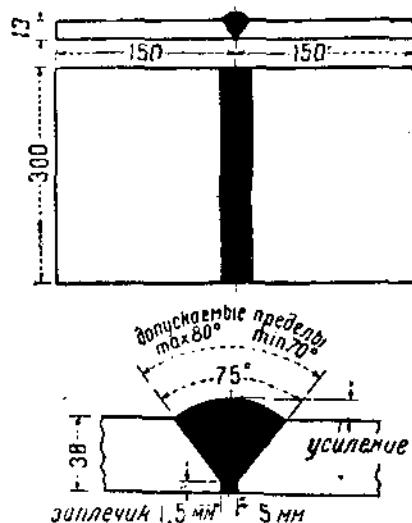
Сварка встык односторонним V-образным швом.
